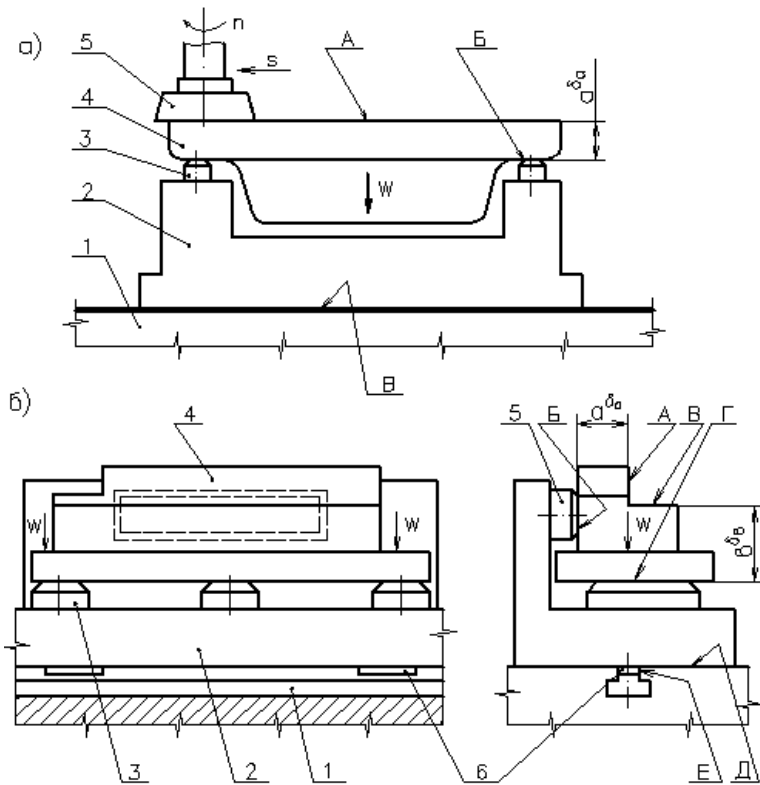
Схемы установки заготовок в приспособлениях при обработке для обеспечения размеров в одном (а) и двух (б) направлениях
